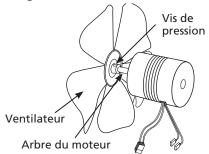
Arbre moteur du ventilateur et emplacement de la vis de pression
